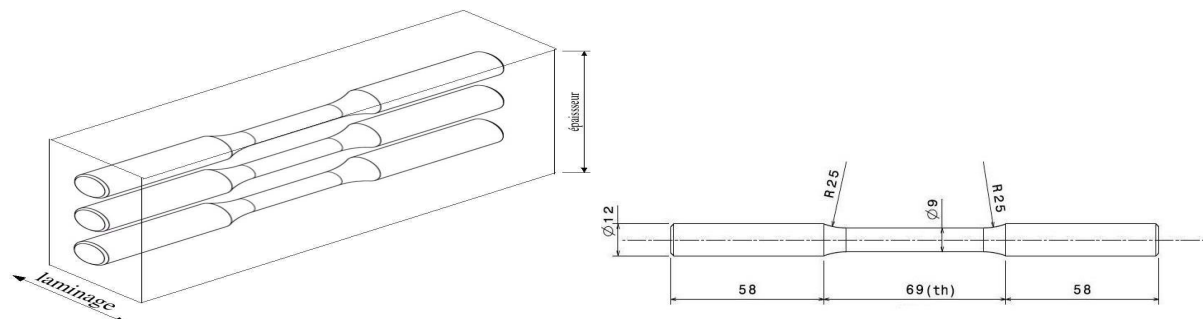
Sens de prélèvement et géométrie des éprouvettes de fatigue de flexion rotative
